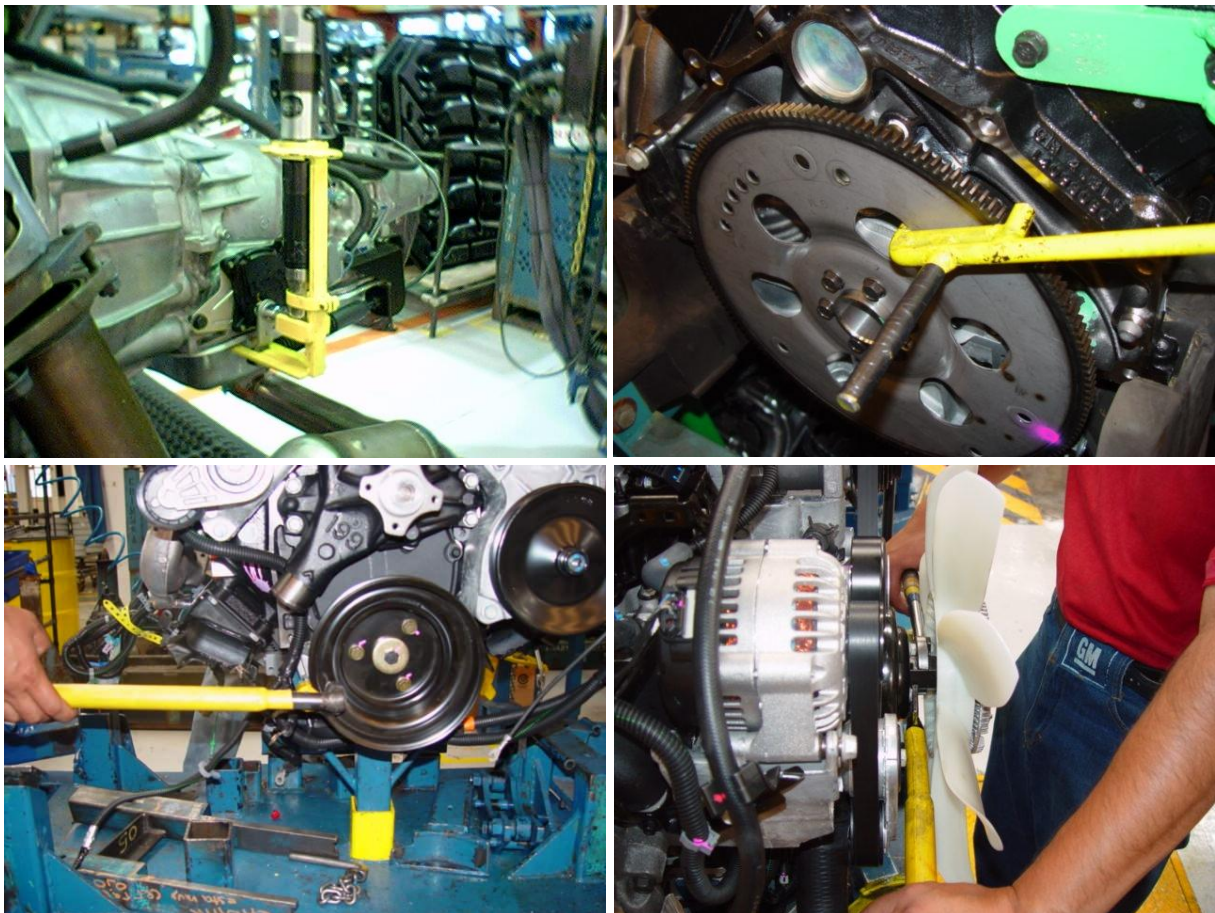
Diferentes palancas para el ensamble de componentes a lo largo de la línea.
